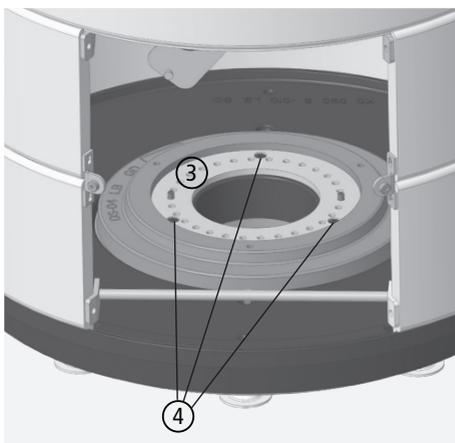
Retirer la rondelle de réglage des butées latérales
